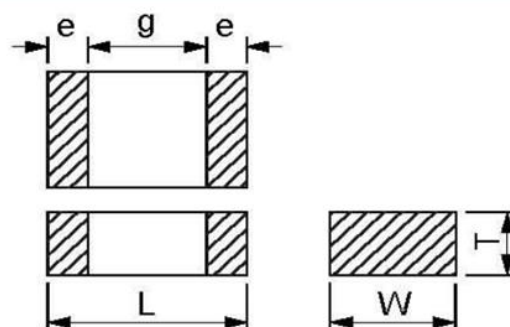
Цоколевка и размеры конденсаторов
